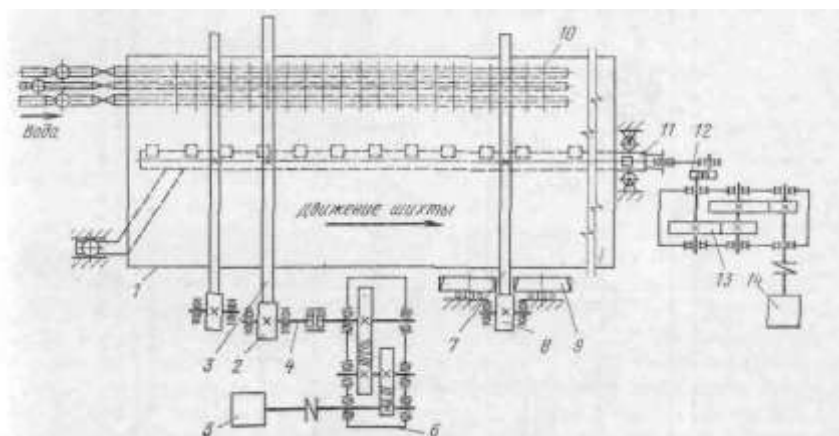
Кинематическая сема привода барабанного смесителя
